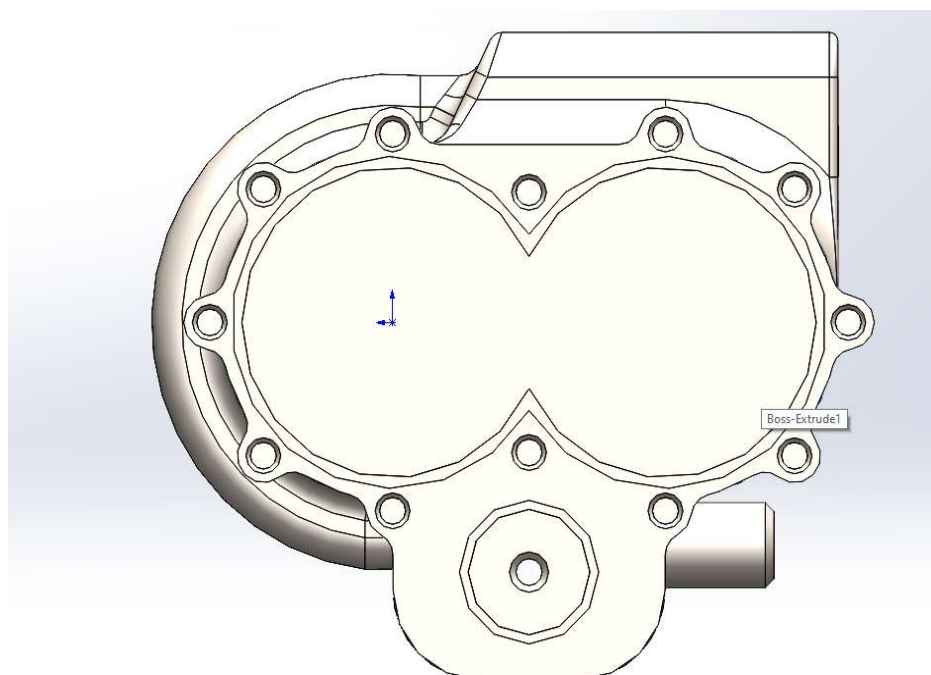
Трьох вимірна модель корпусу вид спереду
